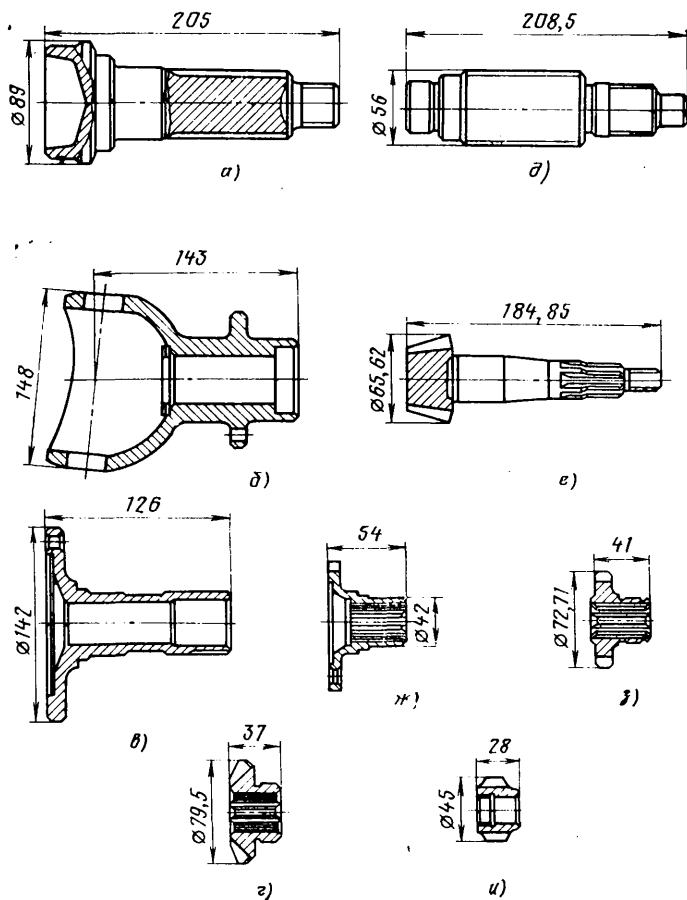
Перспективная номенклатура деталей для изготовления холодной объемной штамповкой:
